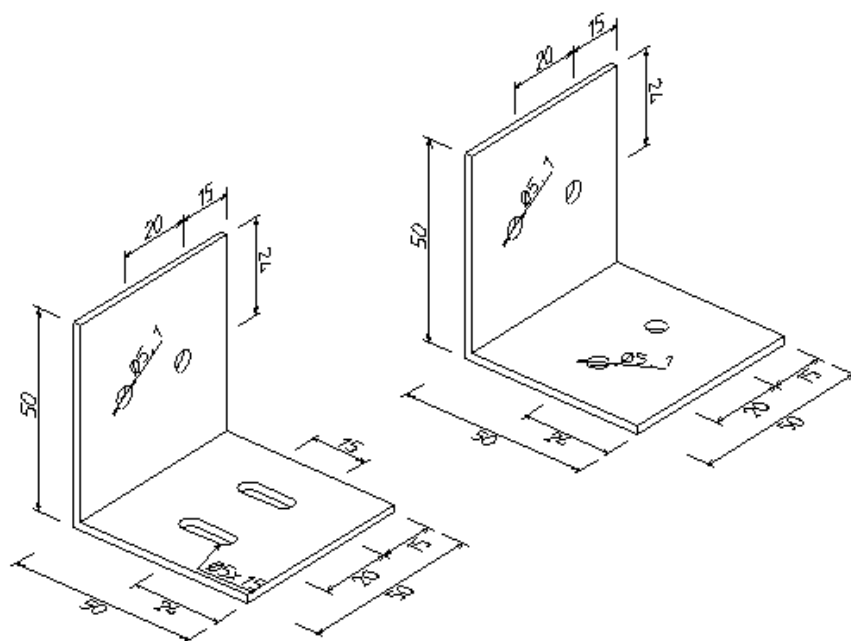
Patte de fixation des profilés horizontaux sur les profilés verticaux
